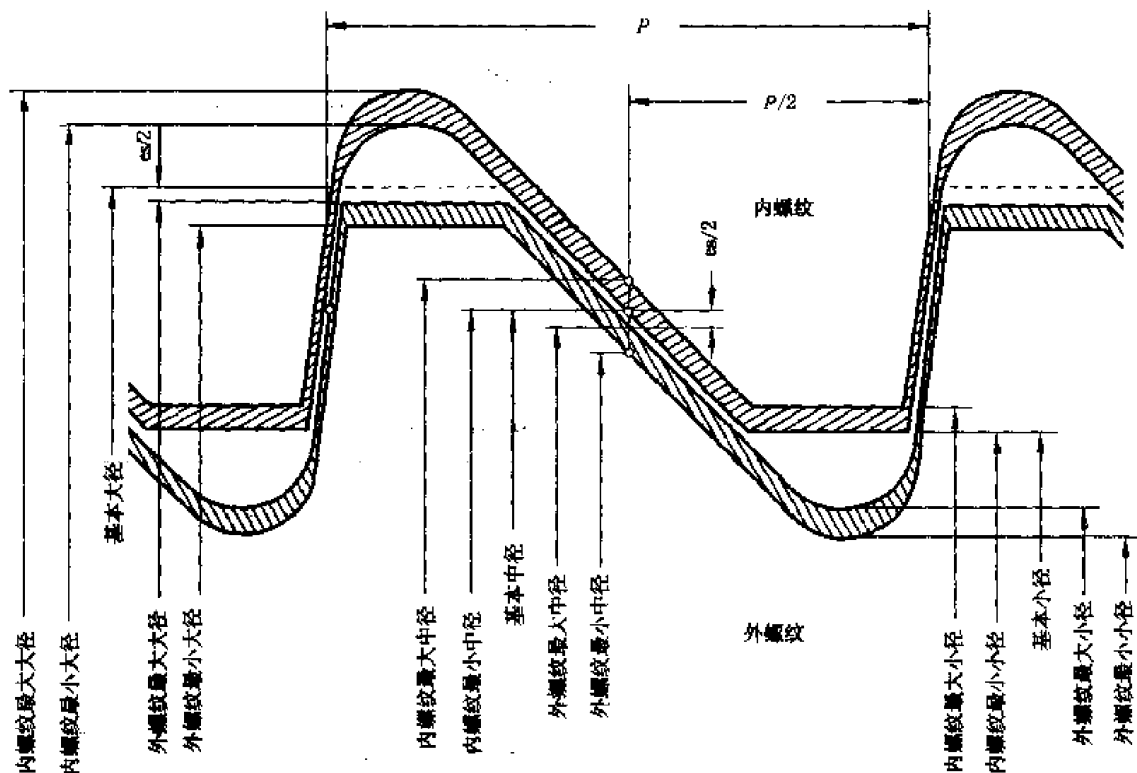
英制锯齿形螺纹的公差带位置
